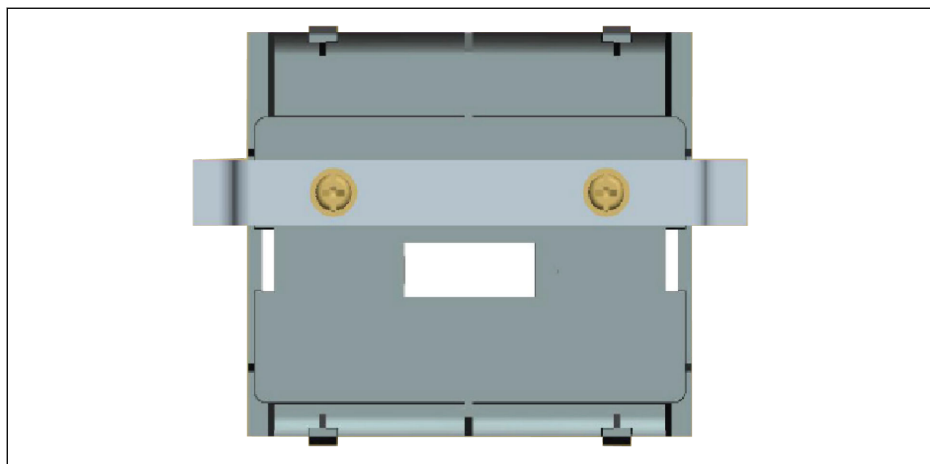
Montageplatte befestigen (Rückansicht)
